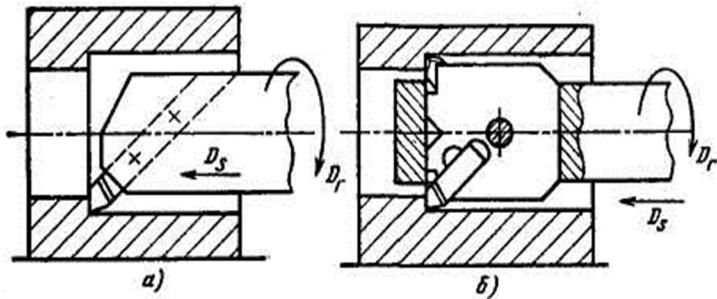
Схема растачивания отверстий резцом и плавающим блоком
